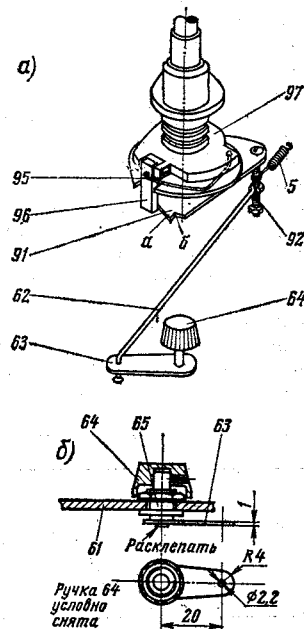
Кинематическая схема механизма повторного воспроизведения (а) и узел ручки управления (б): 5 — пружина; 61 — панель; 62 — тяга; 63 — рычаг; 64 — ручка управления; 65 — втулка резьбовая (от резистора СП); 91 — рычаг; 92 — винт М3×10; 95 — пружина защелки; 96 — защелка; 97 — блок кулачков.
